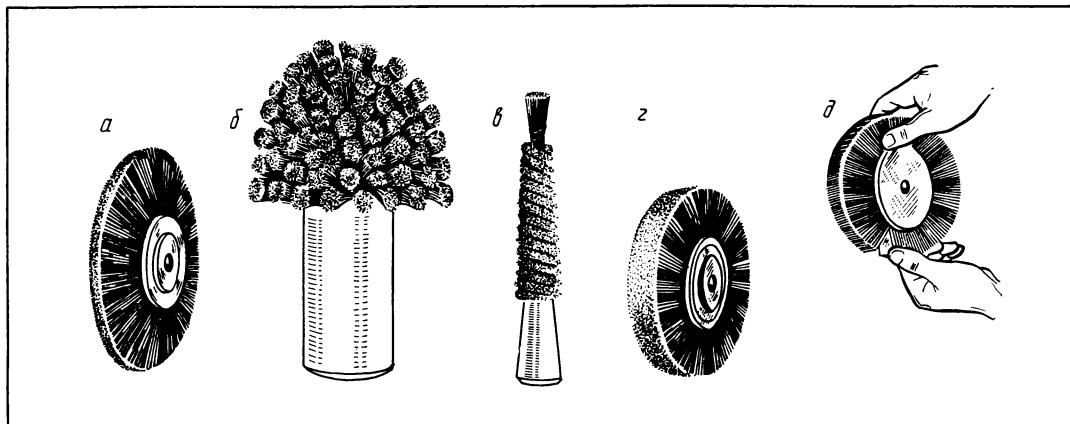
Полировочные круги и насадки для шлифовально-полировального станка и бормашины:
